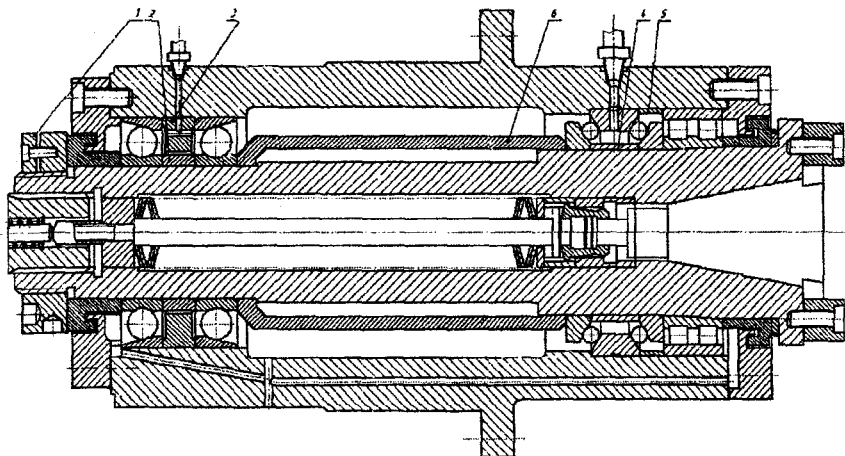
Шпиндельный узел с комплектом шарикового упорно-радиального подшипника с углом контакта 60° типа 178800 и роликового радиального цилиндрического типа 3182100 в передней опоре и с шариковыми радиально-упорными подшипниками со схемой дуплекс О-образный – в задней
